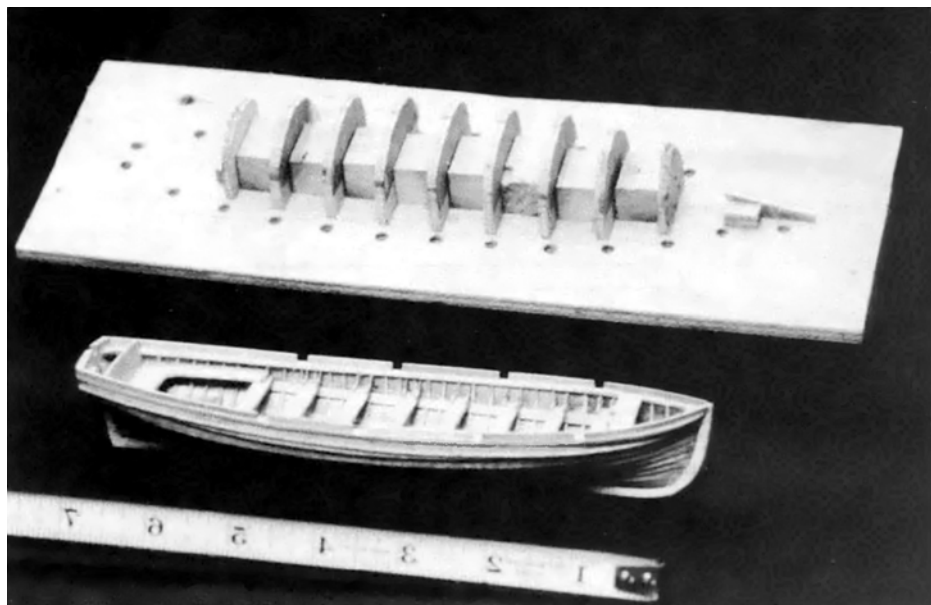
Приспособление для изготовления шлюпок Портии Такакджан (Фотография Стива Сагала).
